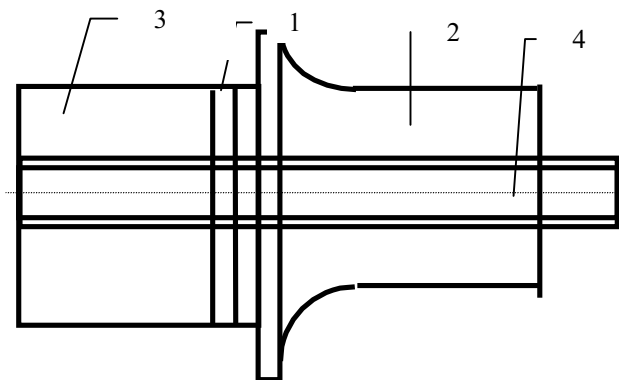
Полуволновой пьезоэлектрический преобразователь
